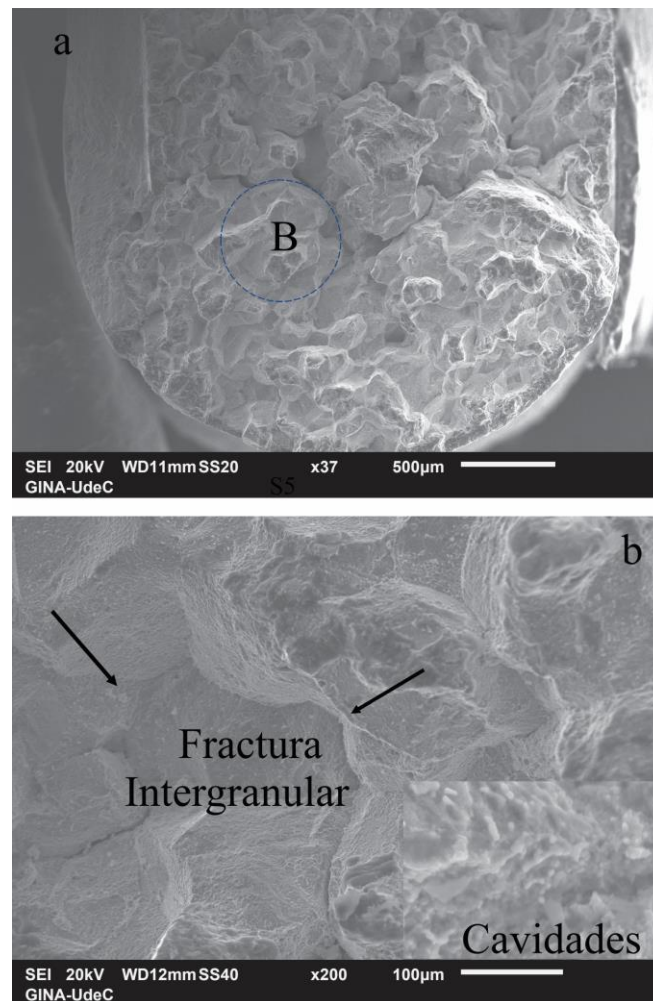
MEB sección de fractura de falla de A2. a) Sección de Fractura, b) Tipo de fractura. Fuente: Elaboración propia.
